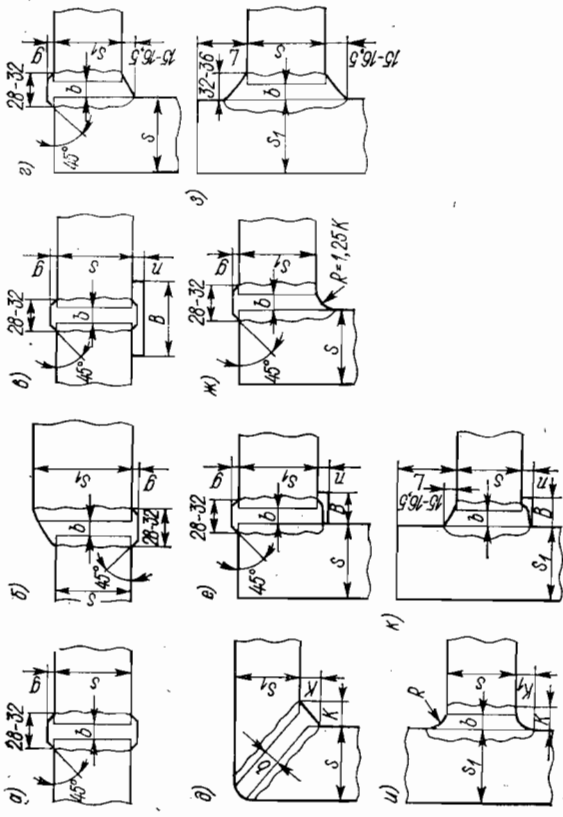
Конструкции стыковых (а—в), угловых (г—ж) и тавровых (з—к) сварных соединений стали, выполненных электрошлаковой сваркой: а — без скоса кромок; б — без скоса кромок неравной толщины; в, е, к — без скоса кромок на приварной подкладке; г, з — без скоса кромок с нормальной галтелью; д — со скосом двух кромок; ж, и — без скоса кромок с увеличенной галтелью
